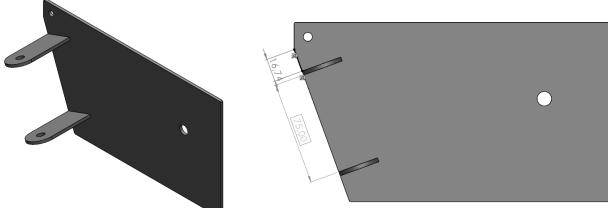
Unión mediante soldadura de la placa delantera soporte amoladora y las orejas soporte amoladora. Fuente: elaboración propia.
